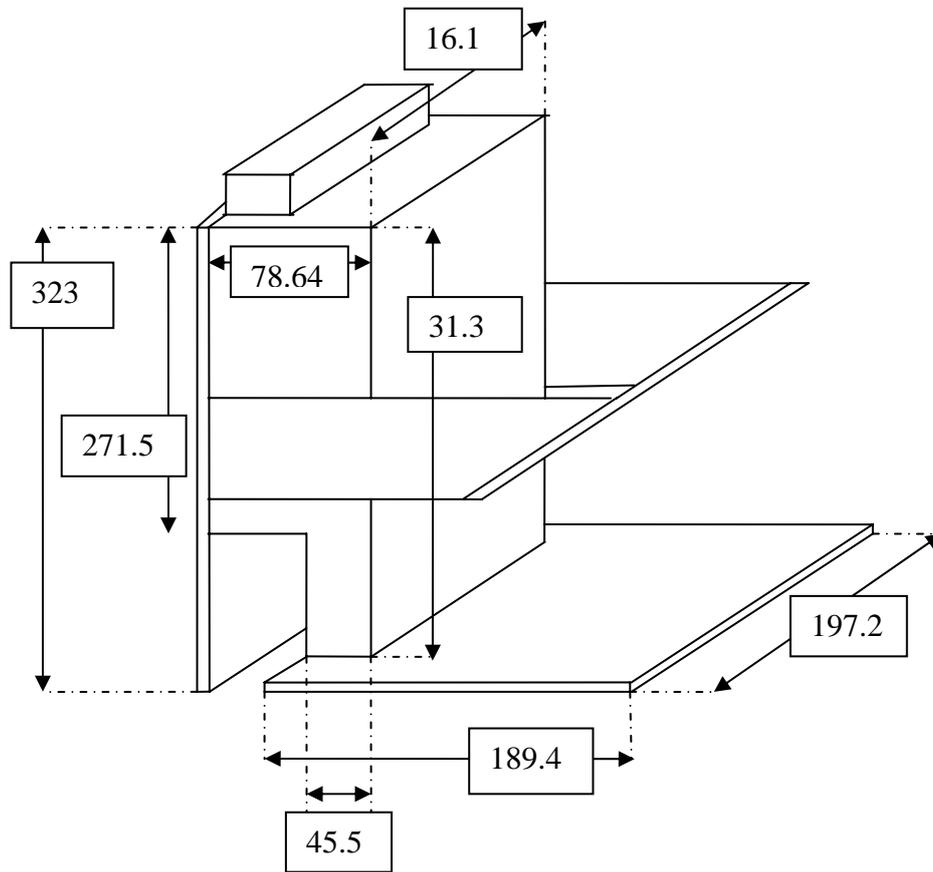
Se puede ver en este diseño la caja del CCD vista de lado con sus dimensiones en milímetros.
